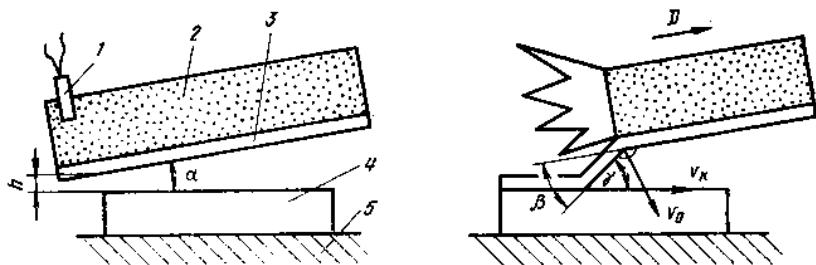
Схема сварки взрывом под углом:
